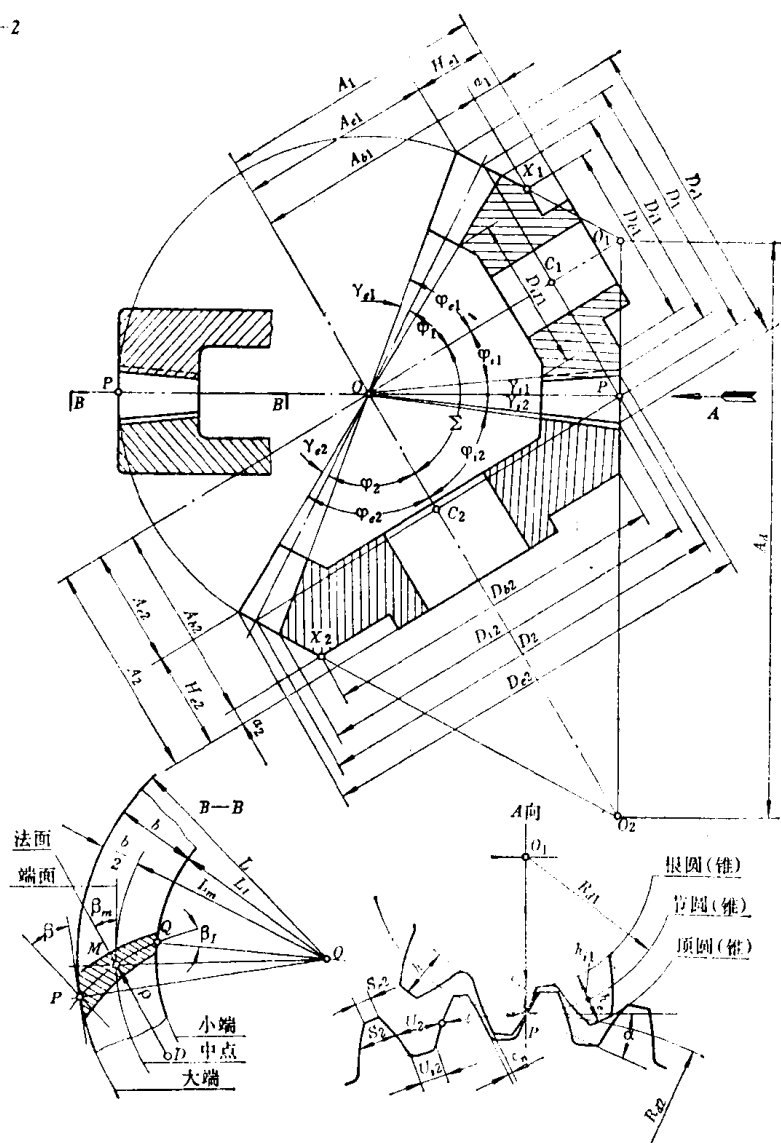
圆锥齿轮副的要素和各部位尺寸
